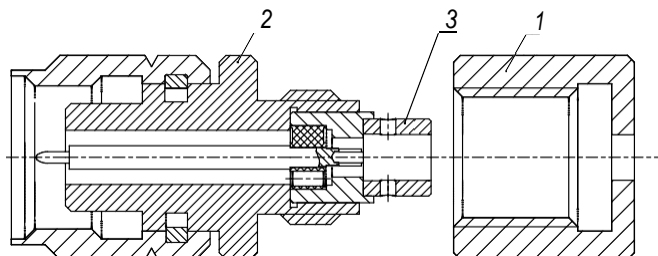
Кабельный соединитель ВК1-40-05-2 с отсоединенной стягивающей гайкой
